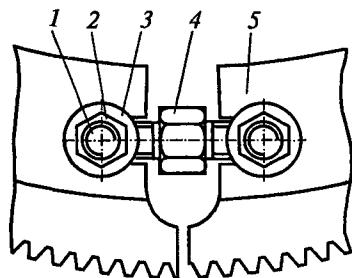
Разжимное устройство траверсы электродвигателя ДТК-800КЭ:
